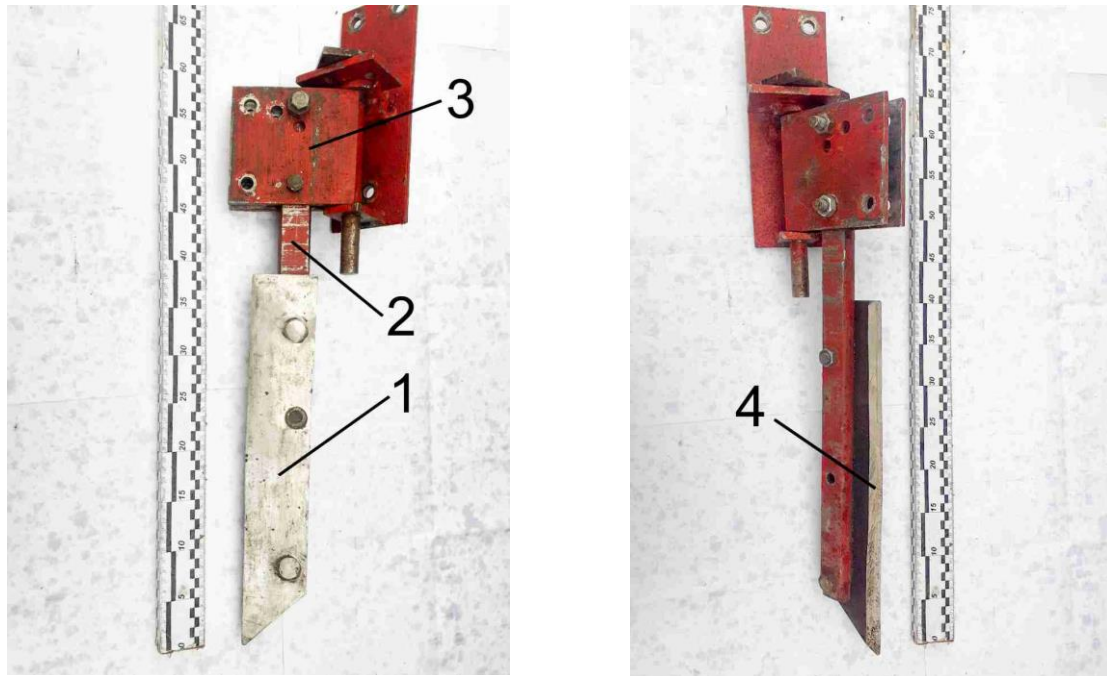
Загальний вид макетного зразка робочого органу глибокорозпушувача: 1 – леміш; 2 - стійка; 3 – пристрій регулювальний; 4 – лезо.
